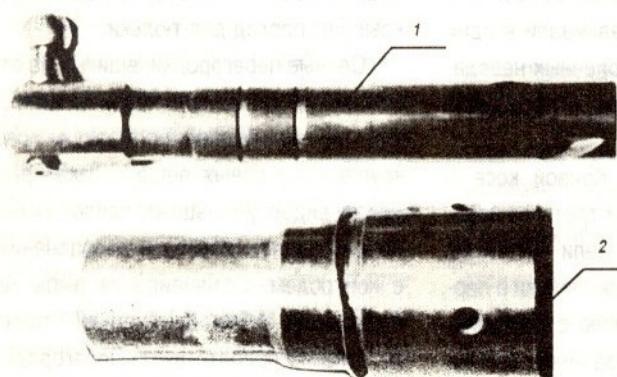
Детали плунжерной пары: 1 – плунжер; 2 – корпус
